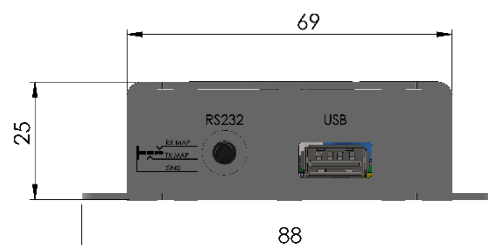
VISTA POSTERIOR COM DIMENSÕES
